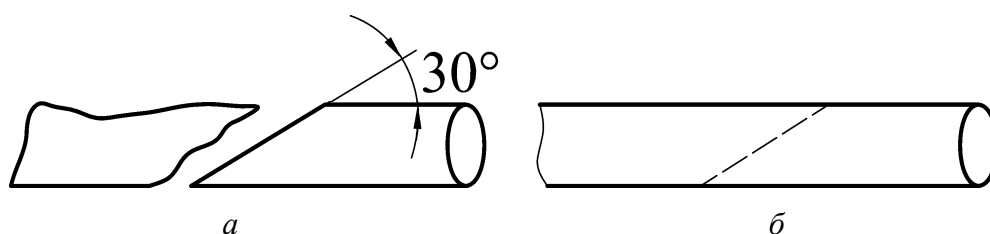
Схема кузнечной сварки: а – до сварки; б – после сварки
